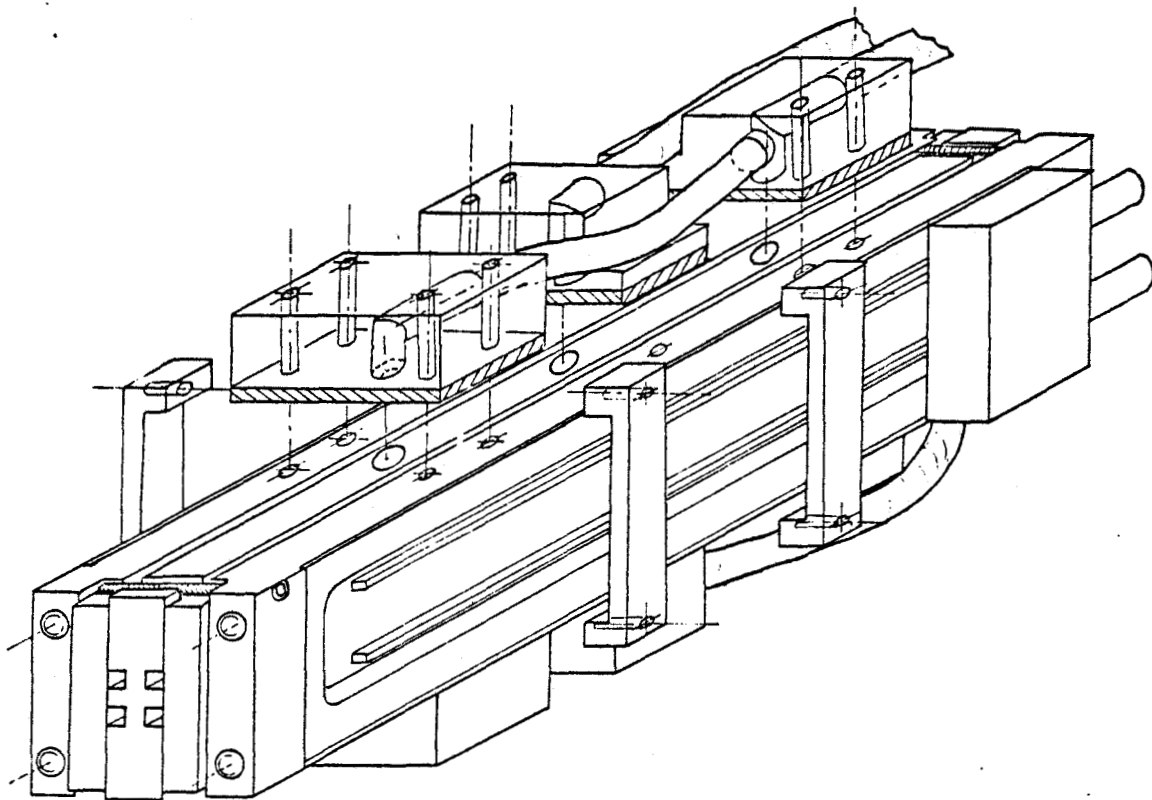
Principe de l'assemblage du deuxième prototype.
